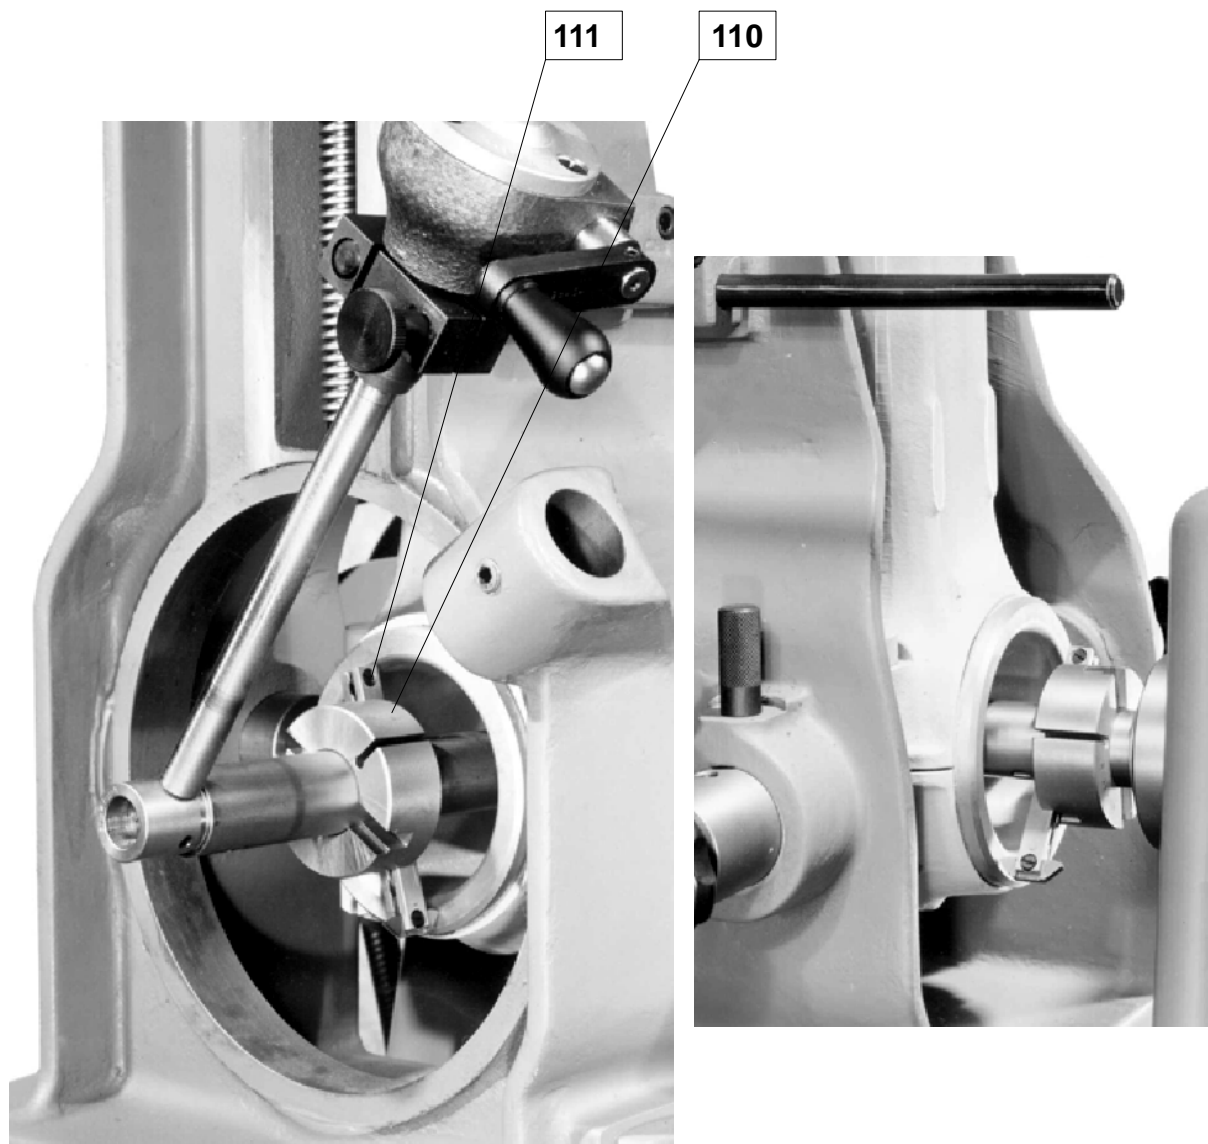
ЦЕНТРОВАЛЬНЫЙ ШПИНДЕЛЬ (ДЕТАЛИ)
